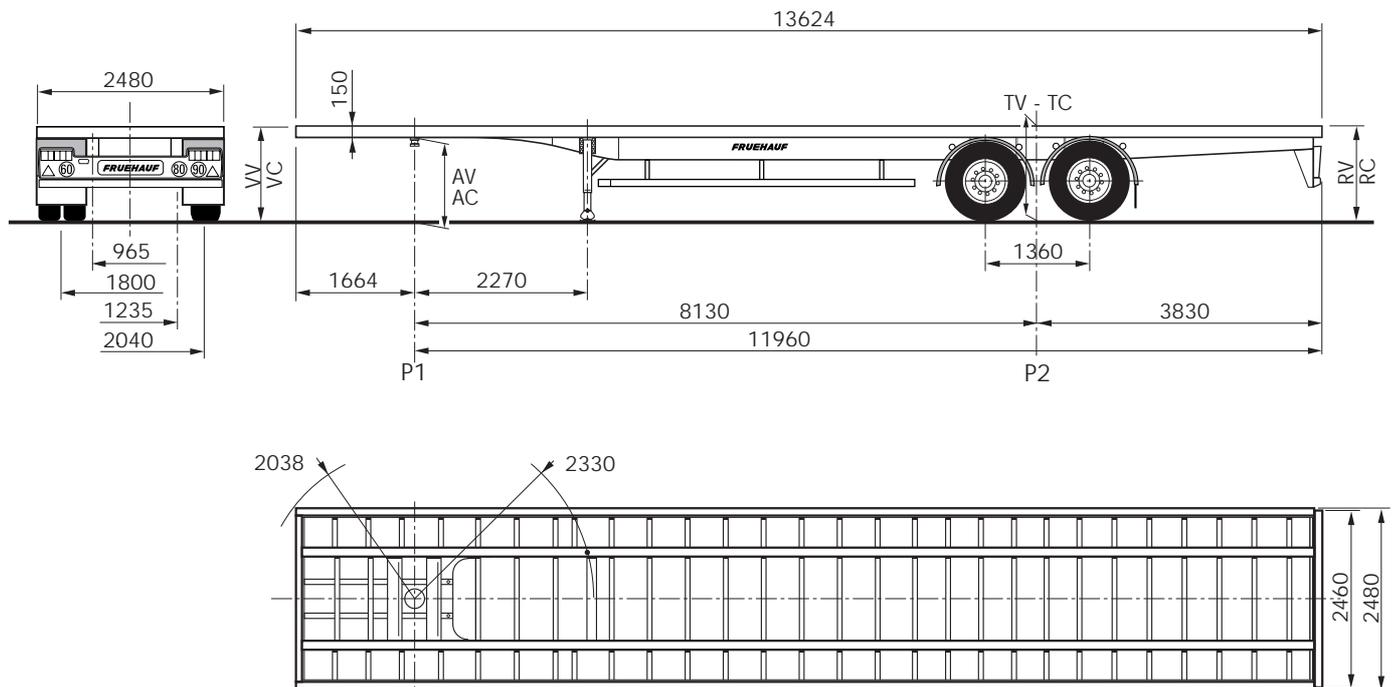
### PLATEAU DROIT Tandem 13,62 m - PTAC 27 ou 32 t
